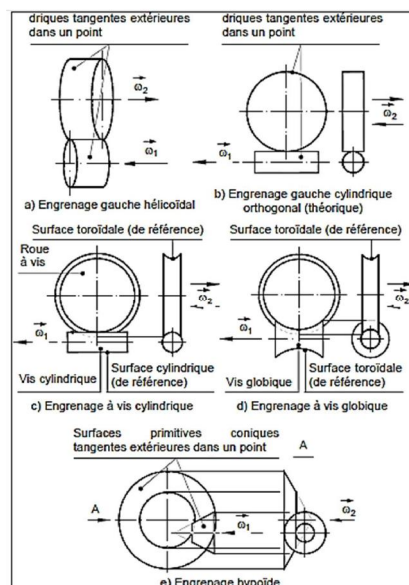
Surfaces primitives ou de références pour des engrenages dégénérés de l'engrenage gauche hyperboloïdal
